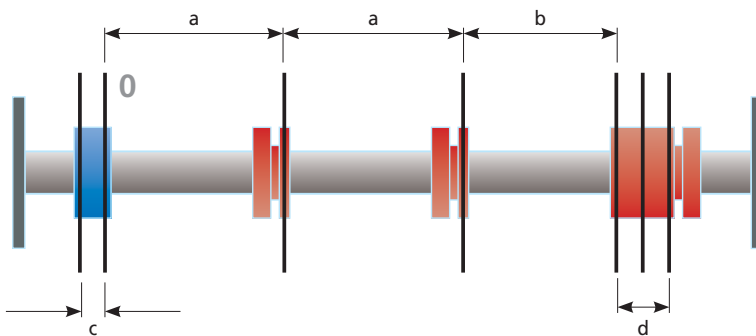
Verstellbarer Einhang mit einer festen und drei beweglichen Sägebüchsen
